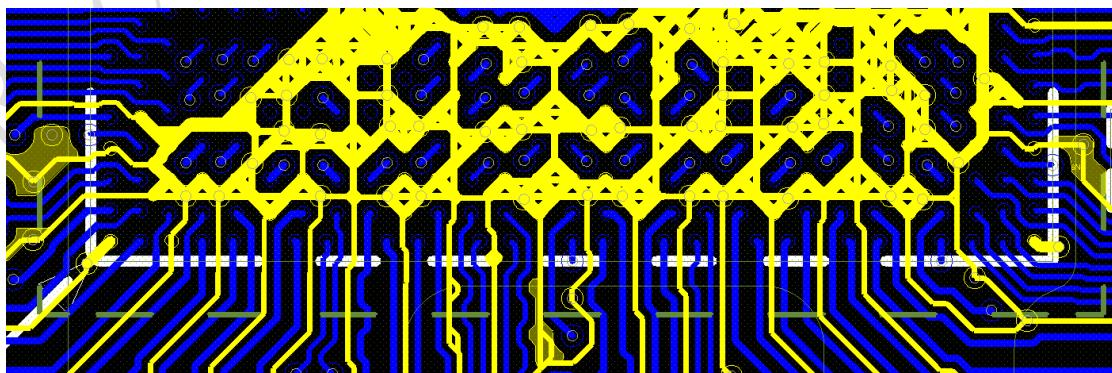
6 层通孔 PCB 模板主控区域过孔设计
